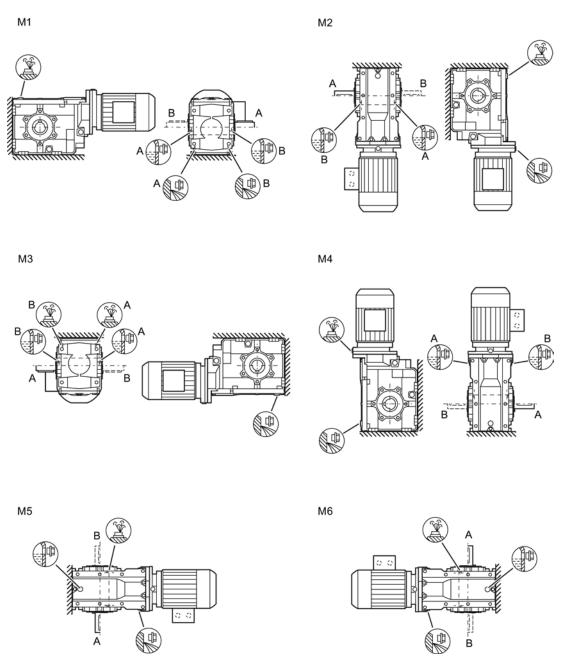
Posiciones de montaje para reductor de ejes perpendiculares B. en versión con patas, tamaños 39 - 49
